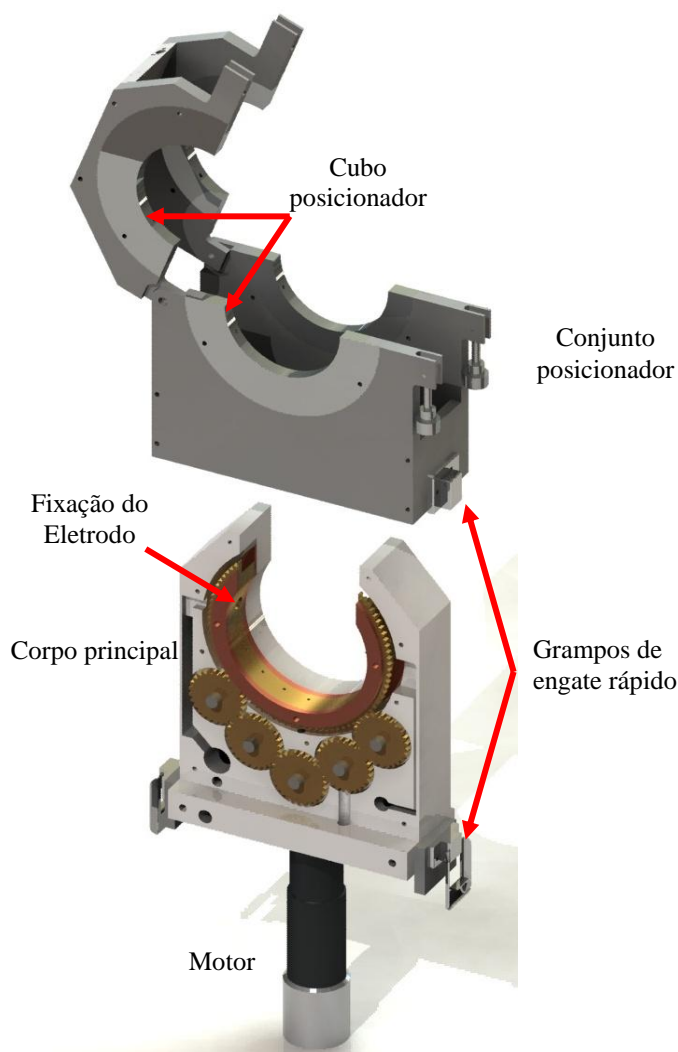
Corpo principal do cabeçote orbital montado e conjunto posicionador.
